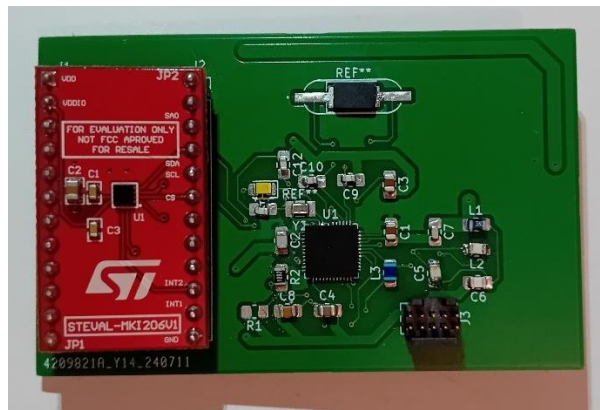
Parte superior BLE\_PCB\_V1 con componentes soldados
